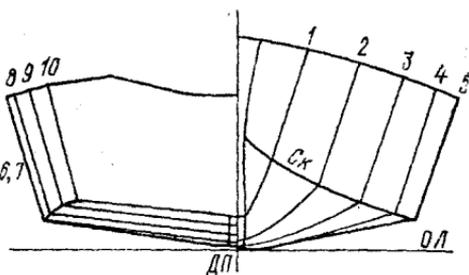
Швертбот «Трепанг» — корпус теоретического чертежа.
